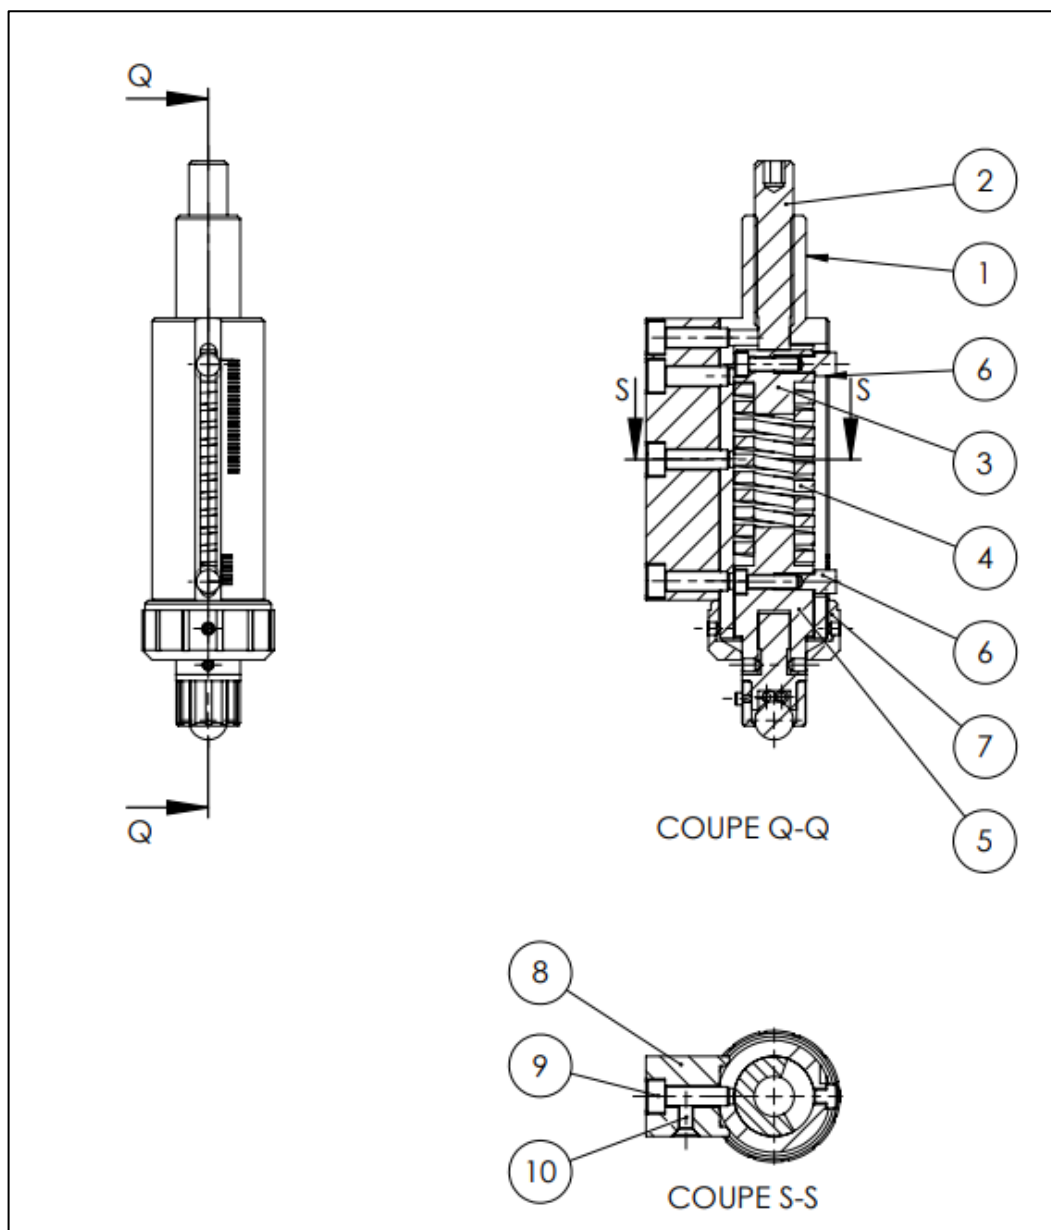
Dessin d'ensemble du dispositif de brunissage
